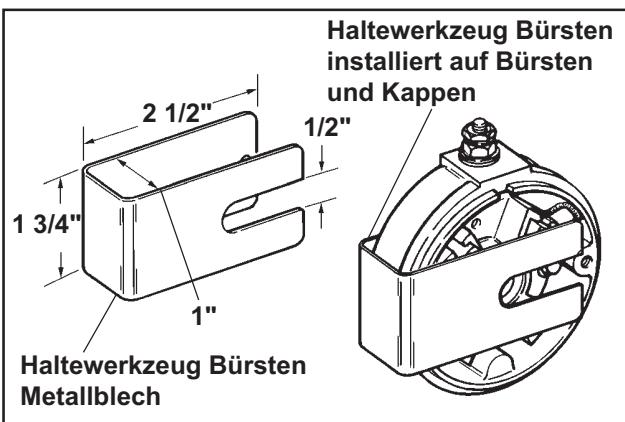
Bürstenhaltewerkzeug (Endkappe Typ "A").
